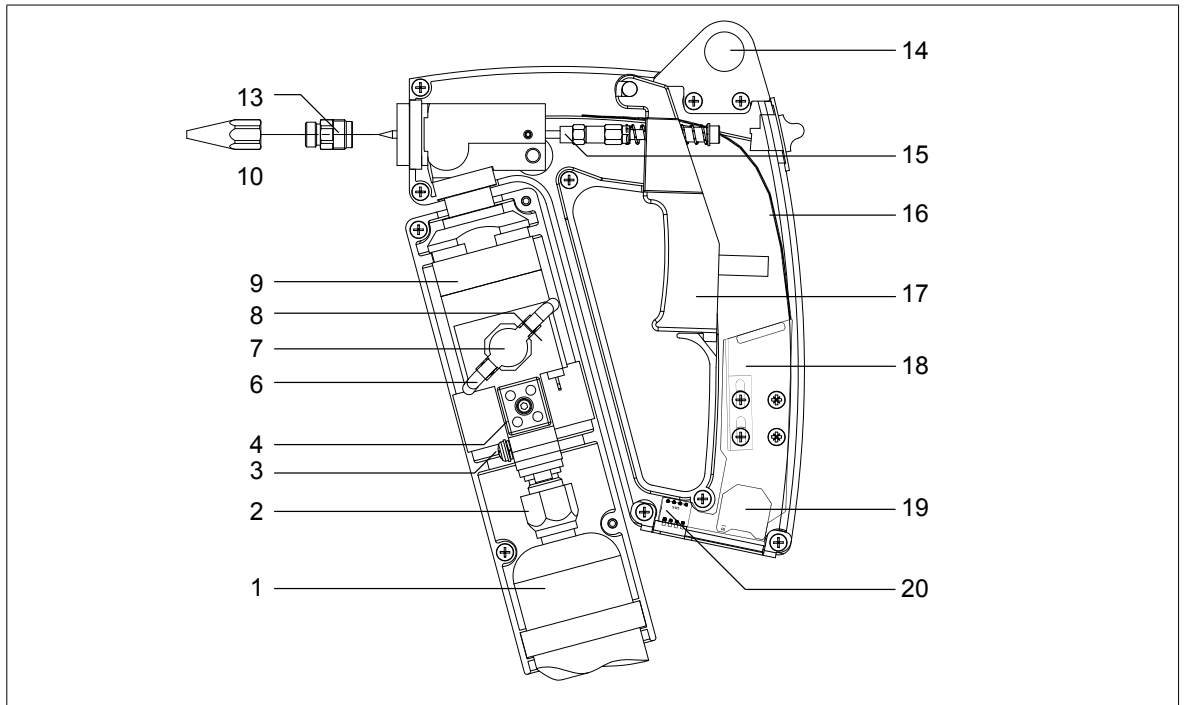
/1: Mechanische opbouw van het pistool type HR
